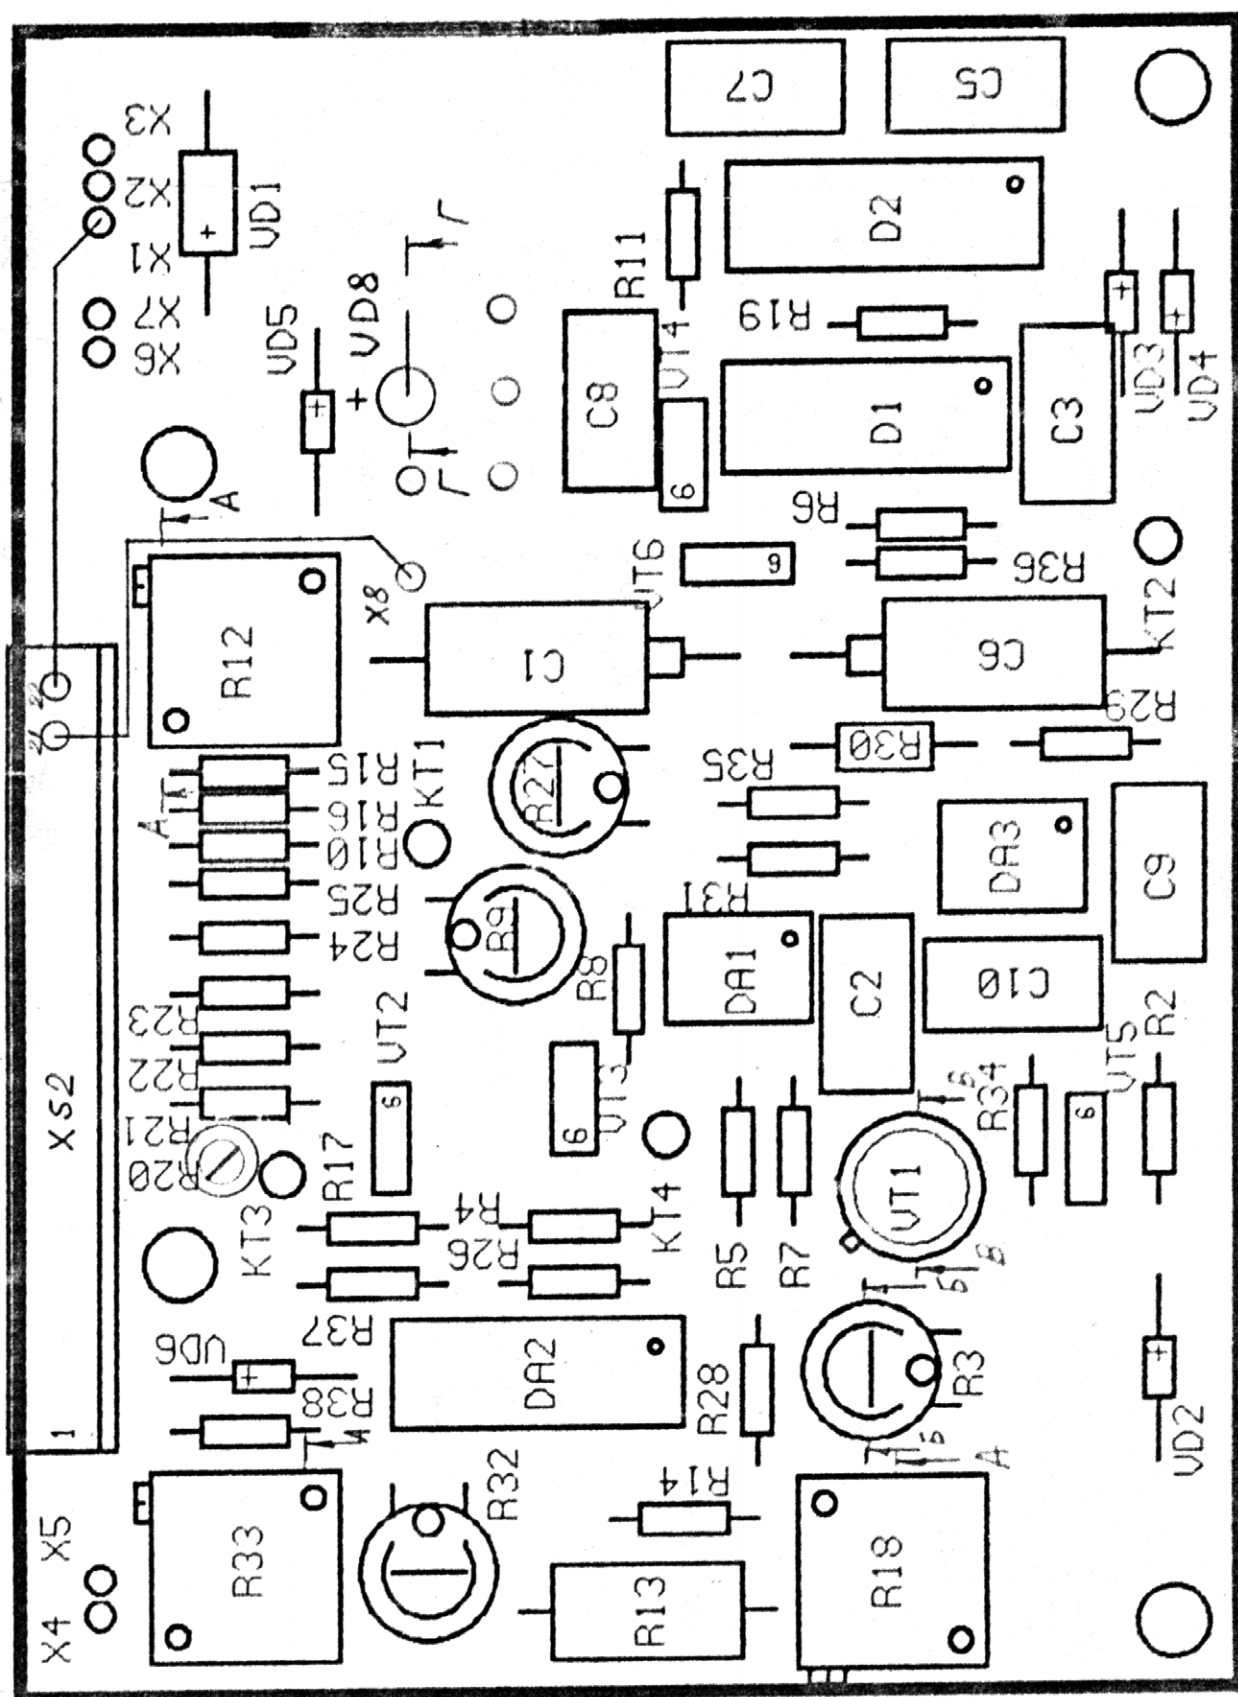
Сборочный чертеж платы обработки ТНГ-94. Вариант исполнения 1. Сторона монтажа.
